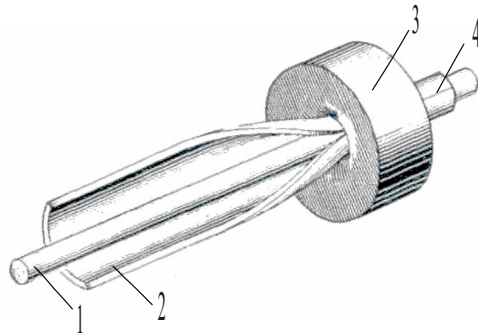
Схема процесу одержання біметалічного дроту сверткою штаби близько сердечника: 1 – сердечник; 2 – штаба, що звивається; 3 – волока; 4 – біметалічний дріт.
